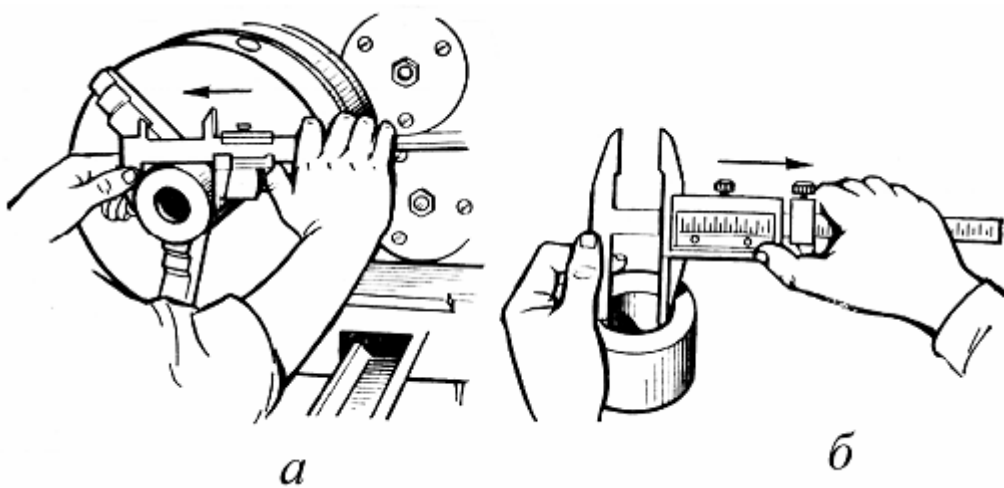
Измерение штангенциркулем наружных (а) и внутренних (б) размеров закрепленной детали
